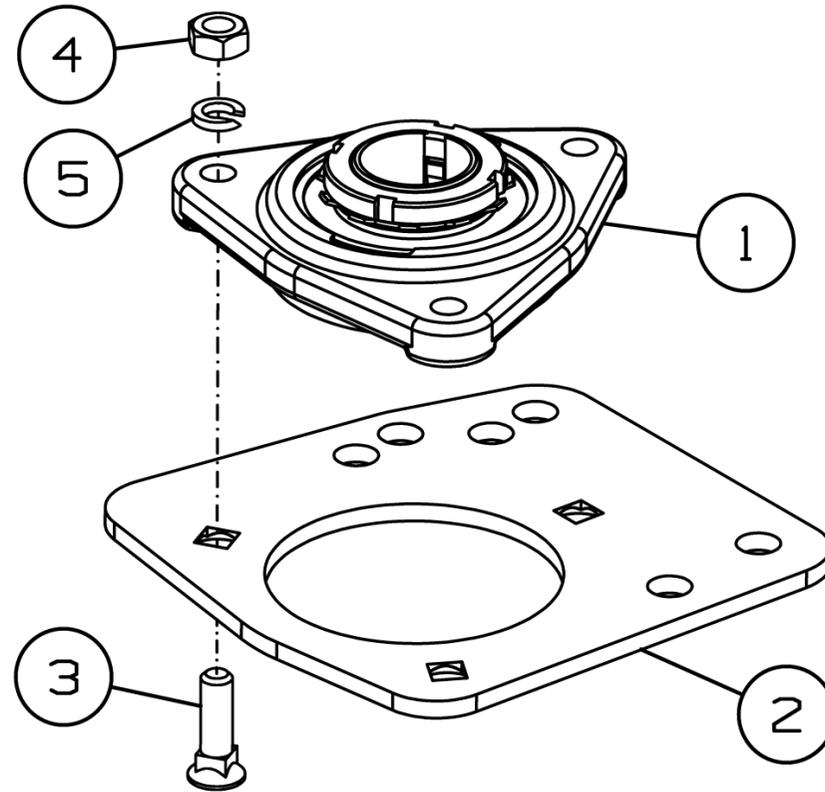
Корпус подшипника SS-780.01.06.140
